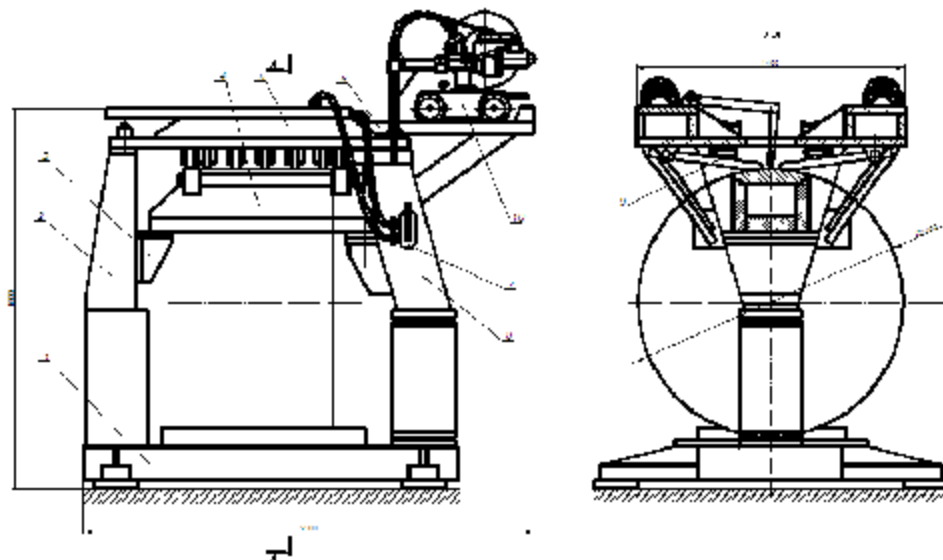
Загальний вигляд установки для зварювання поздовжнього шва обичайки
